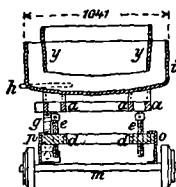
Testring de la coupelle américaine; coupe transversale.
